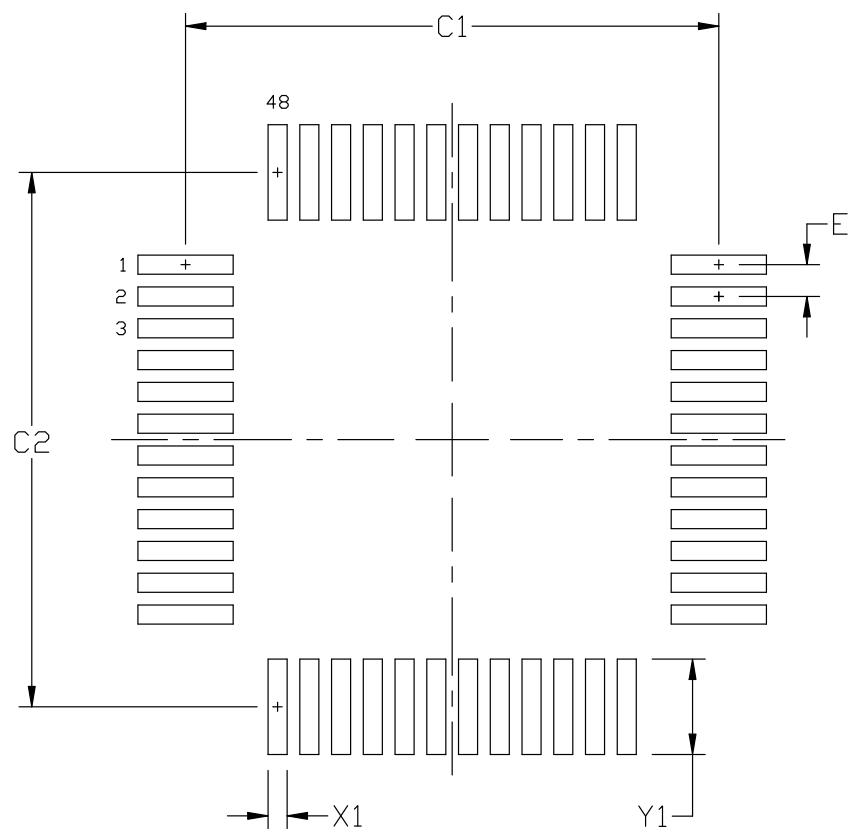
QFP48 PCB 焊盘布局图
